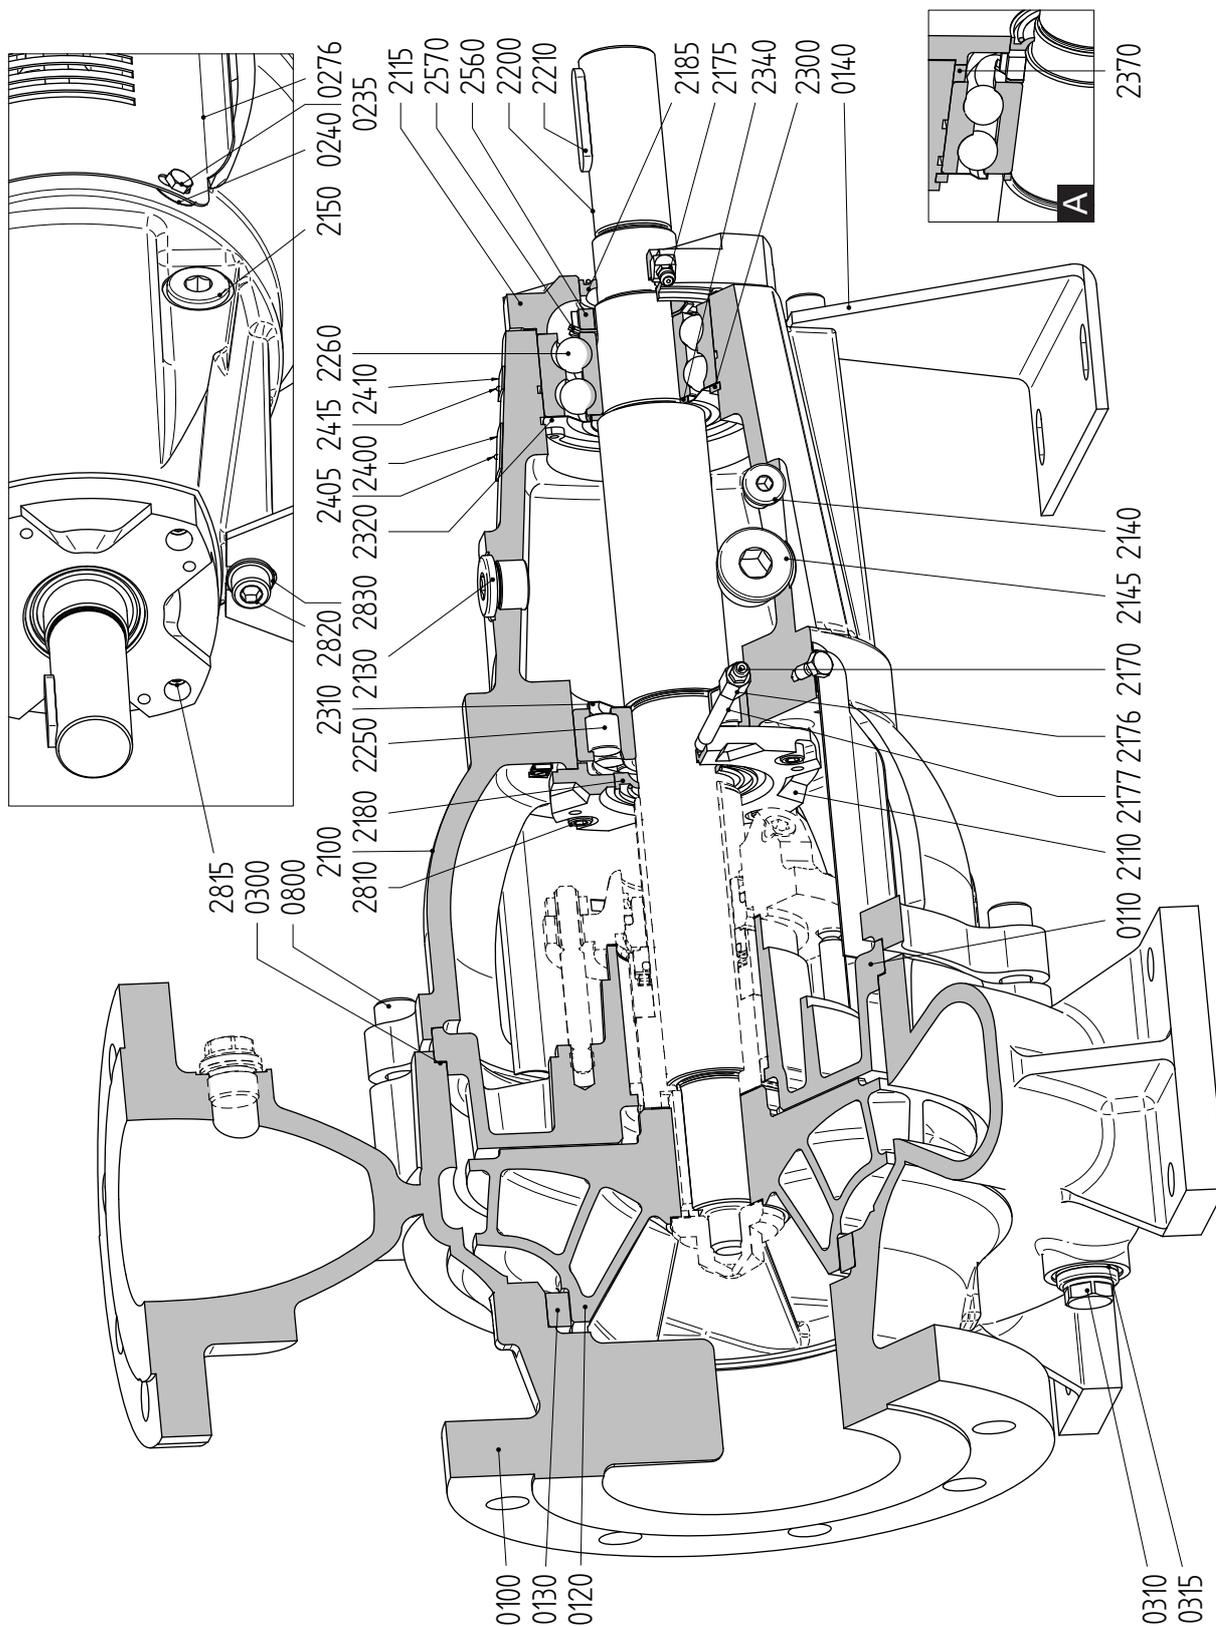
Чертеж в разрезе L2 (A = для группы подшипников 3)
